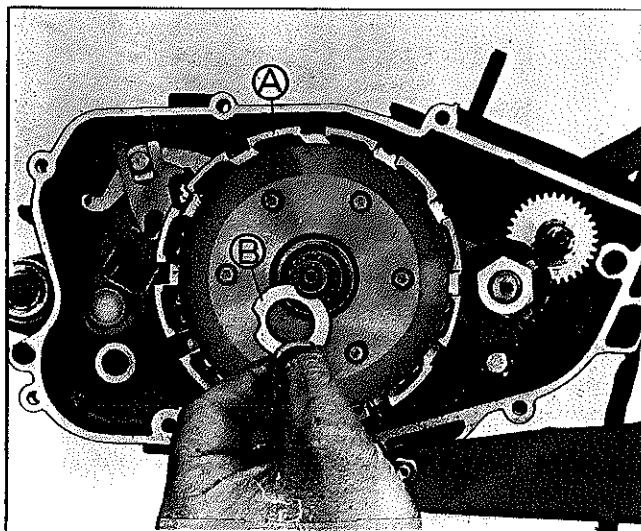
A. CONJUNTO EMBREAGEM CONDUTORA
